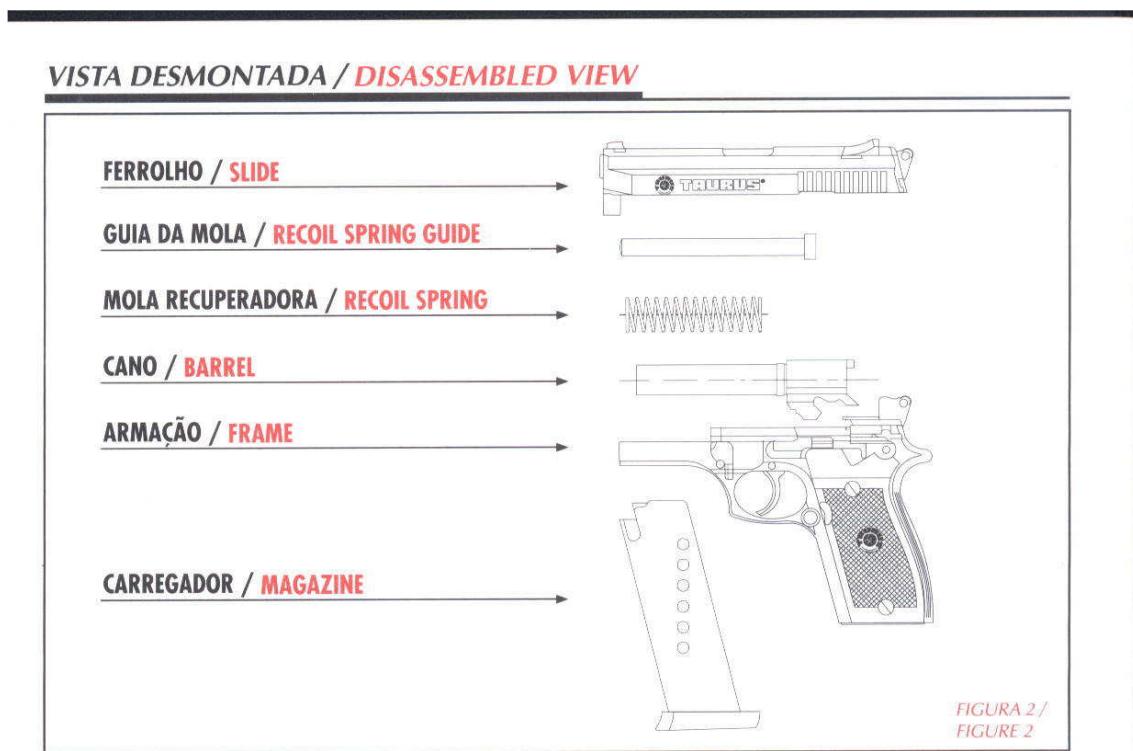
Vista de uma pistola desmontada (Fonte: Taurus).
